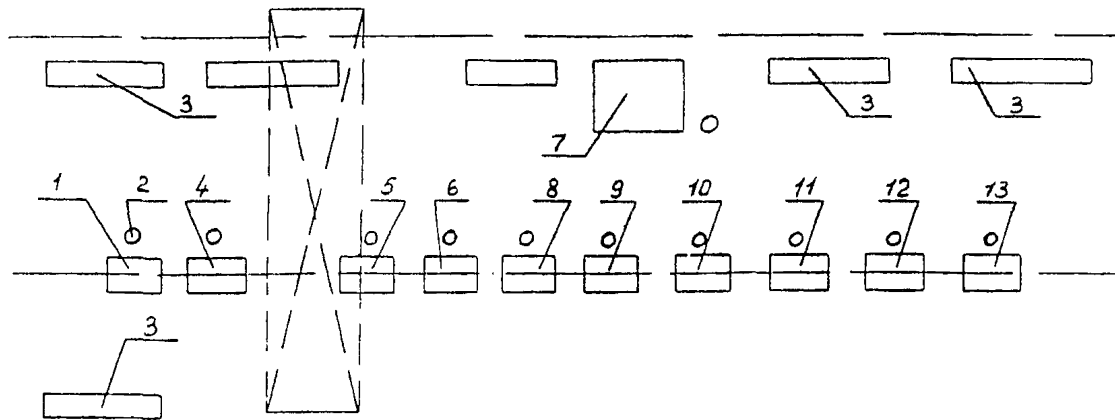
Типовая схема планировки рабочего места общей сборки автомобиля
